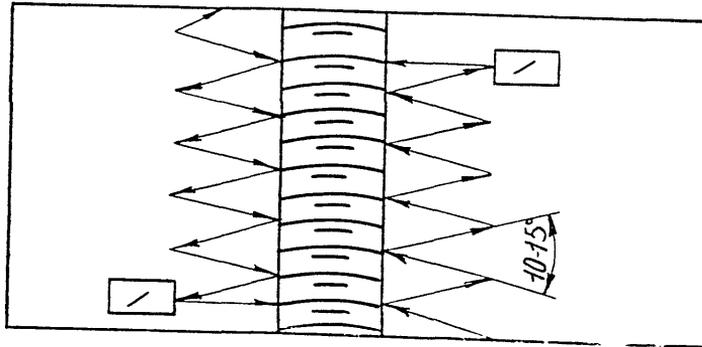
Схема перемещения искателя по поверхности при контроле сварного шва
